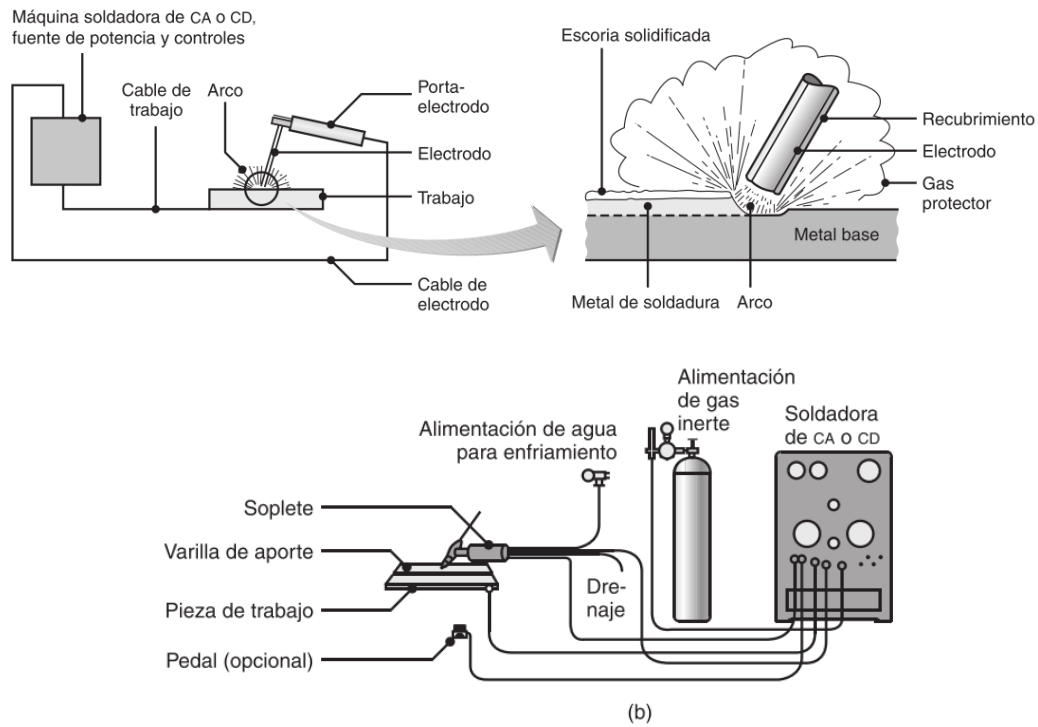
a) proceso de soldadura por arco metálico, b) proceso de soldadura por arco de tungsteno y gas [26].
